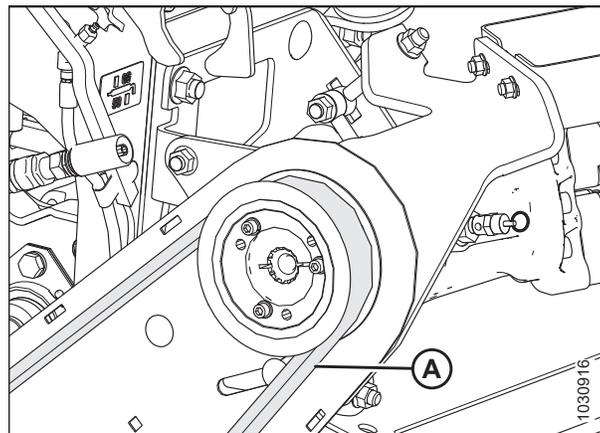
Ведущий шкив — Гидромотор привода плющилки
